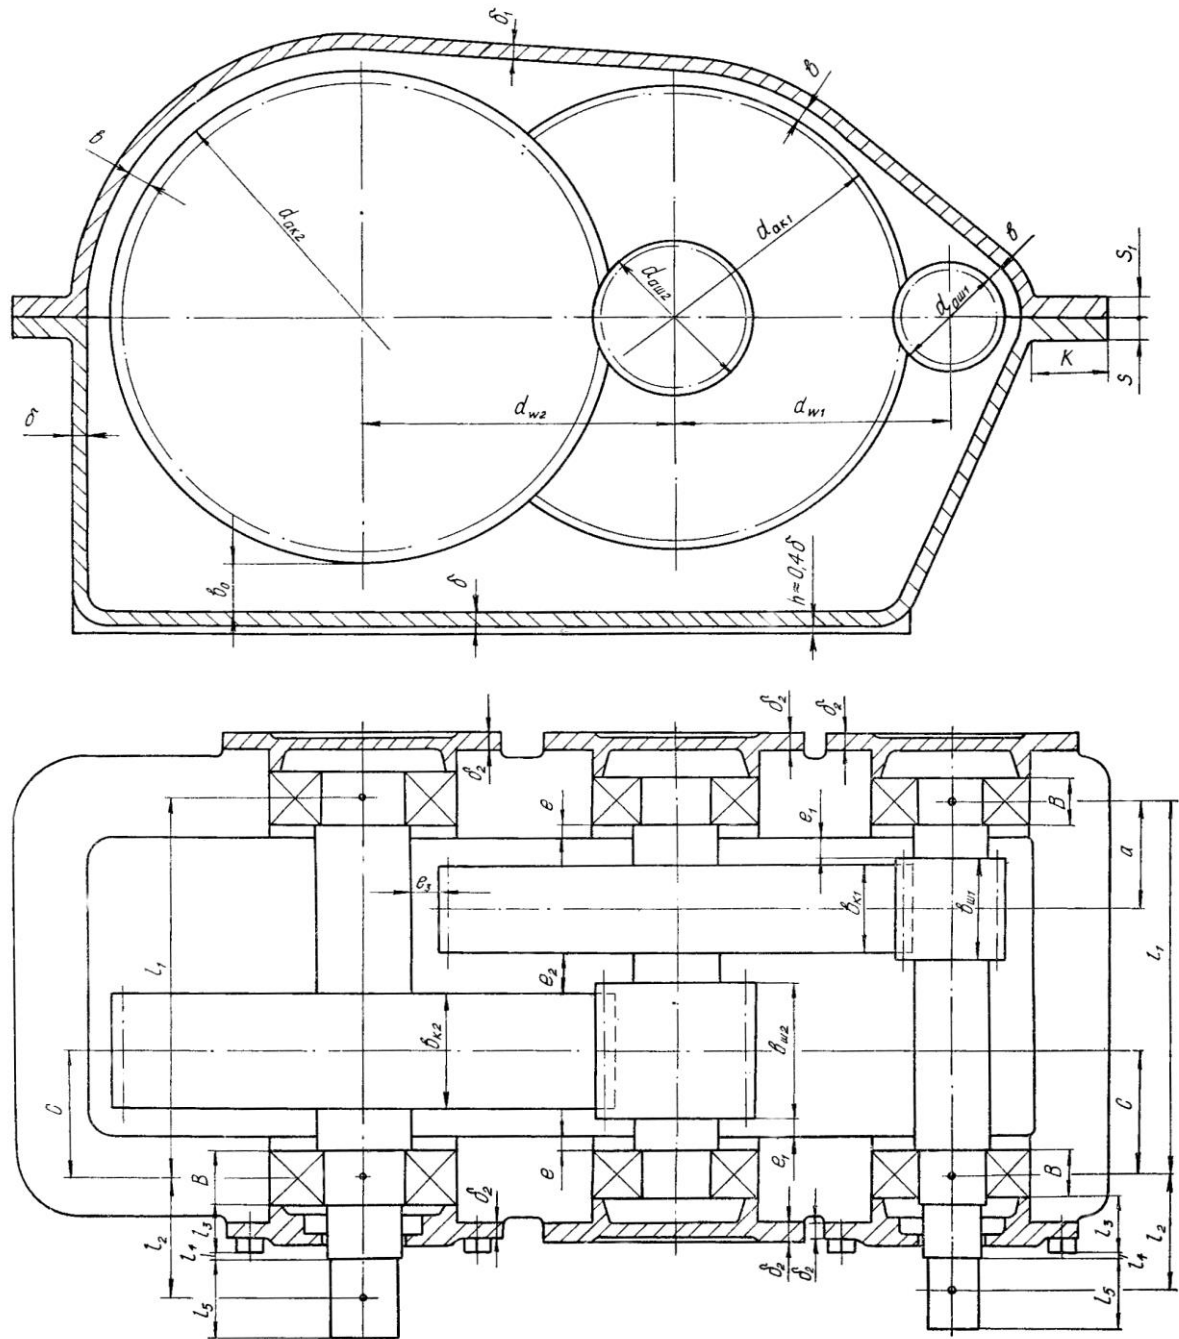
Компонувачне креслення двохступінчатого циліндричного редуктора
